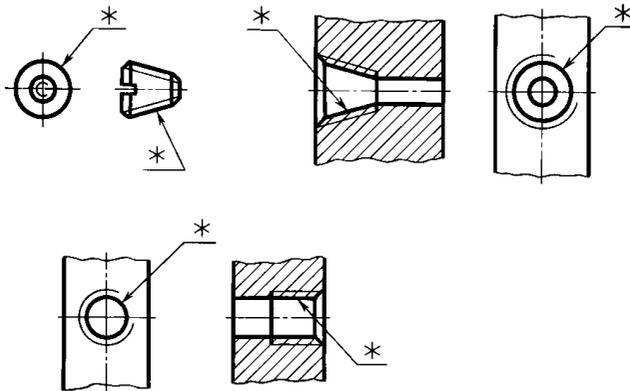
Нанесение конических резьб и трубной цилиндрической резьбы
